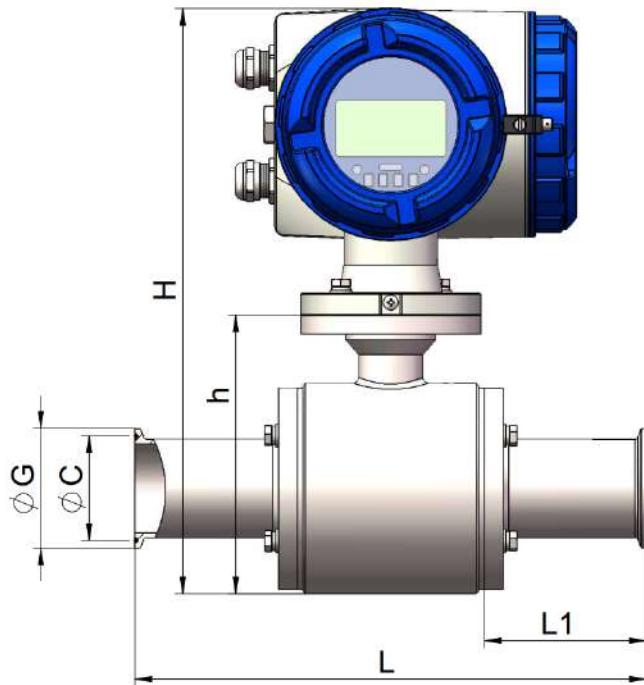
Габаритные размеры первичного преобразователя (тип соединения – кламп)
